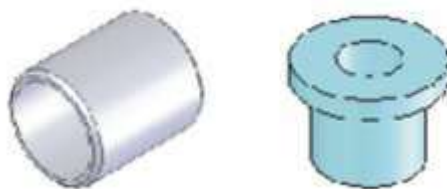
Направляющие детали. Кондукторные втулки. Прижимные детали предназначены для закрепления заготовок в приспособлениях. К этой группе относятся различные прихваты (рис.6) и планки.
